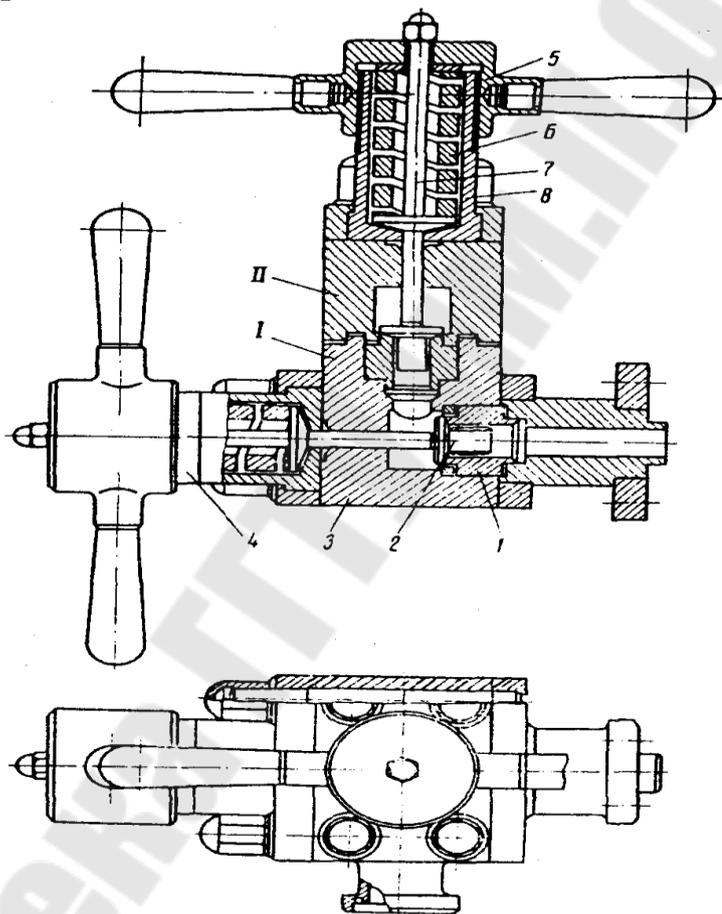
Гомогенизирующая головка: I - первая ступень; II - вторая ступень; 1 - седло клапана; 2 - клапан; 3 - корпус; 4 - нажимное устройство; 5 - накидная гайка; 6 - пружина; 7 - шток; 8 - стакан.
